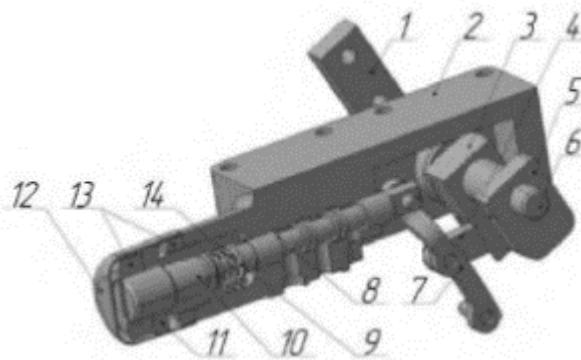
Розподільник системи керування : 1.- планка; 2. - основа; 3. - обмежувач; 4. - шток; 5. – нерухома планка; 6. - регулювальний ролик; 7. – привідна планка; 8. - золотник; 9. - фіксатор; 10,11,14. - регулювальник; 12. - кришка; 13. - гайки
